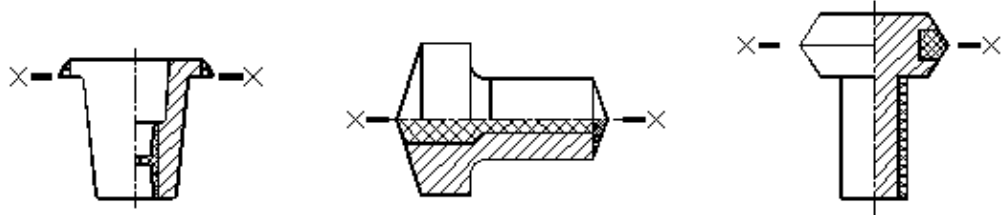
Вплив площини роз'єму штампу на форму штампованої заготовки
